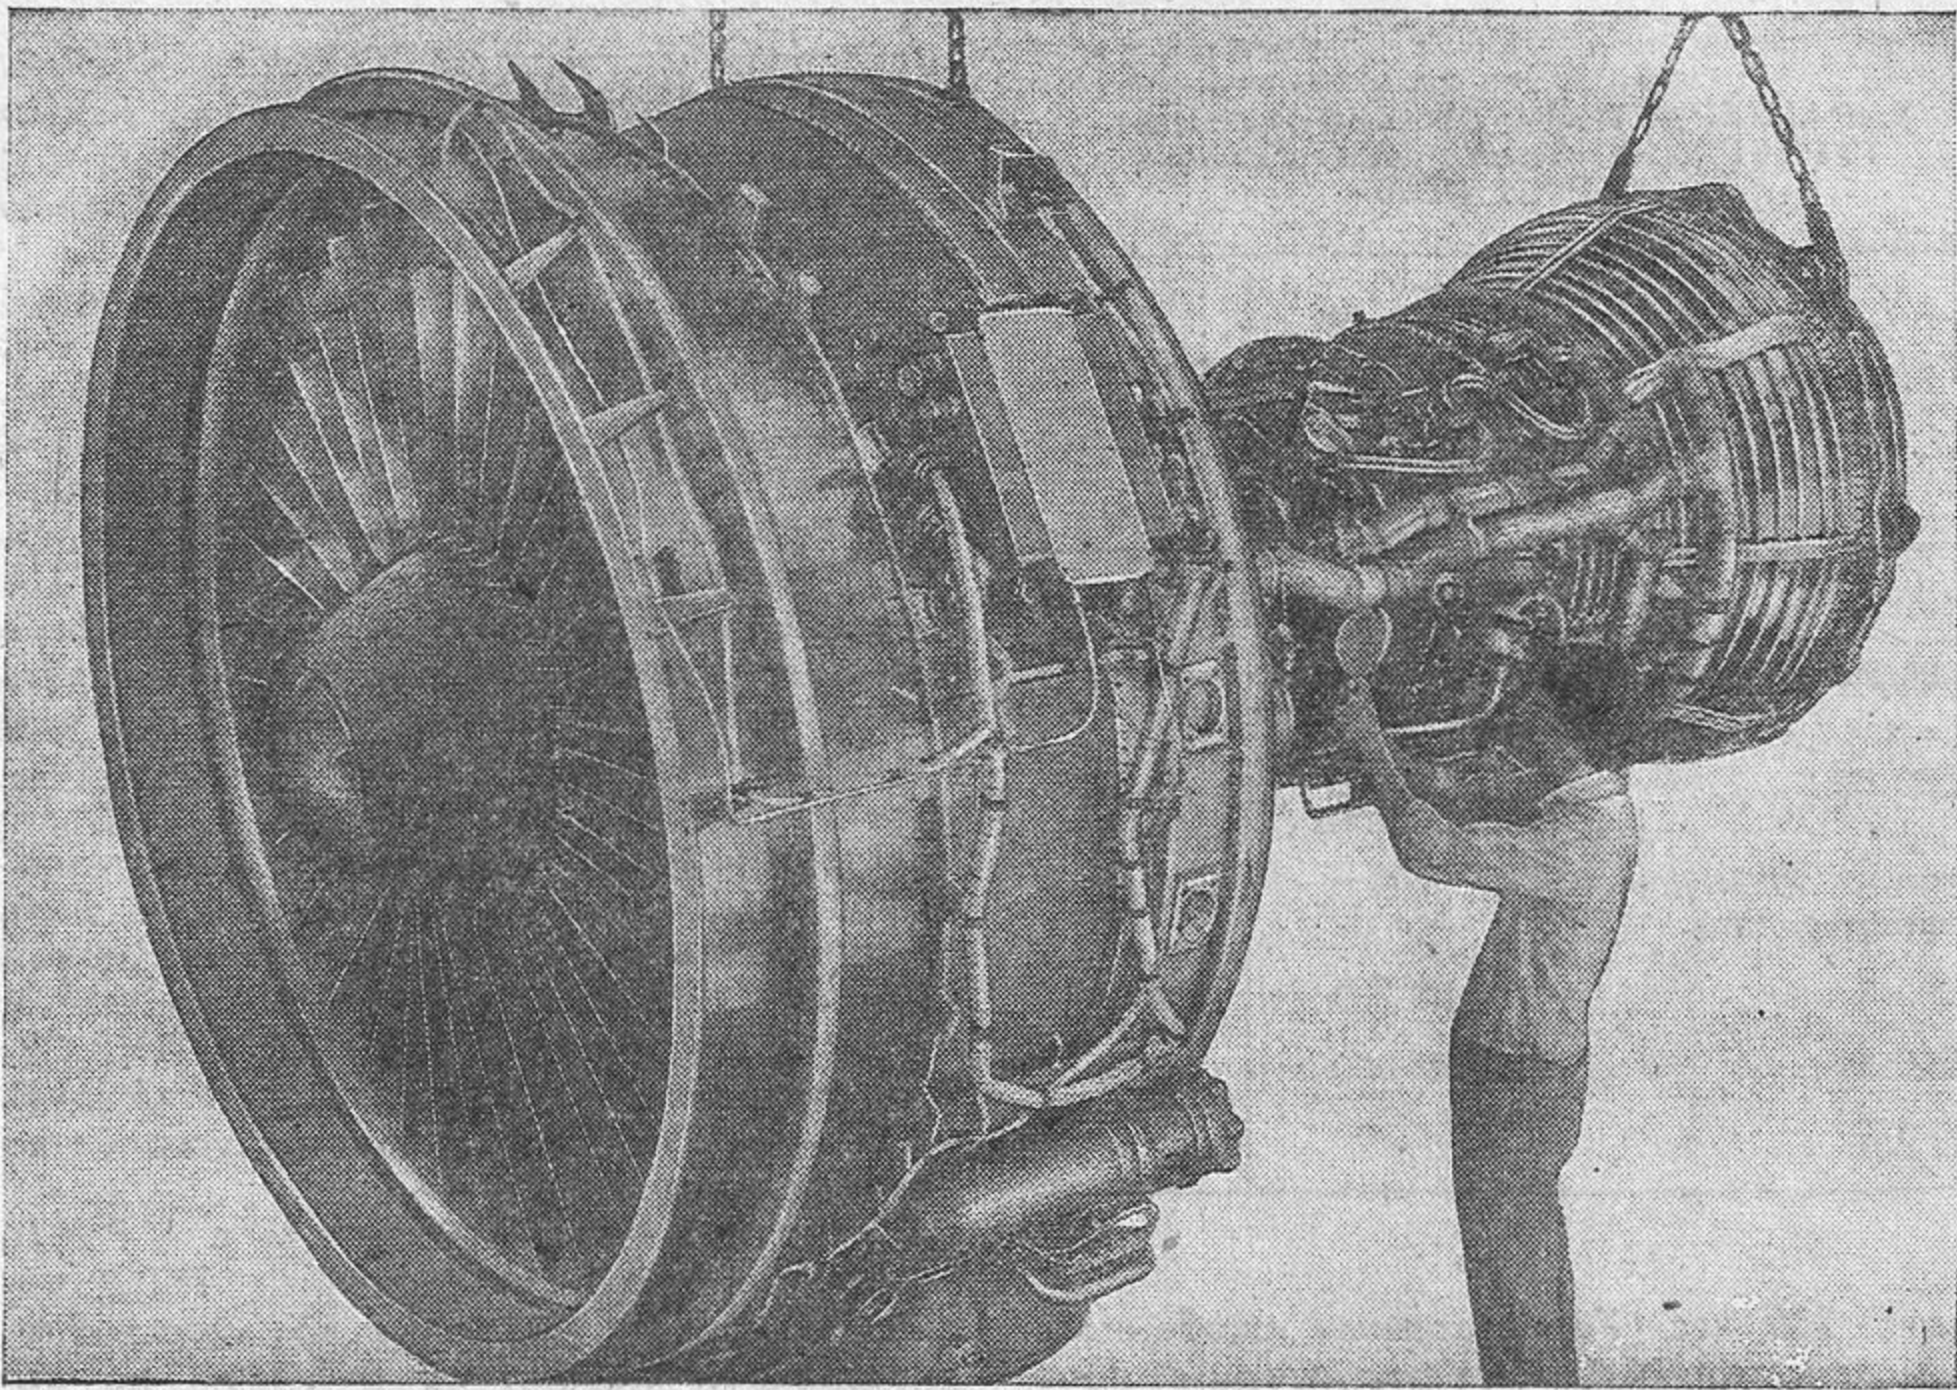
Двухконтурный турбореактивный двигатель F117-PW.100
